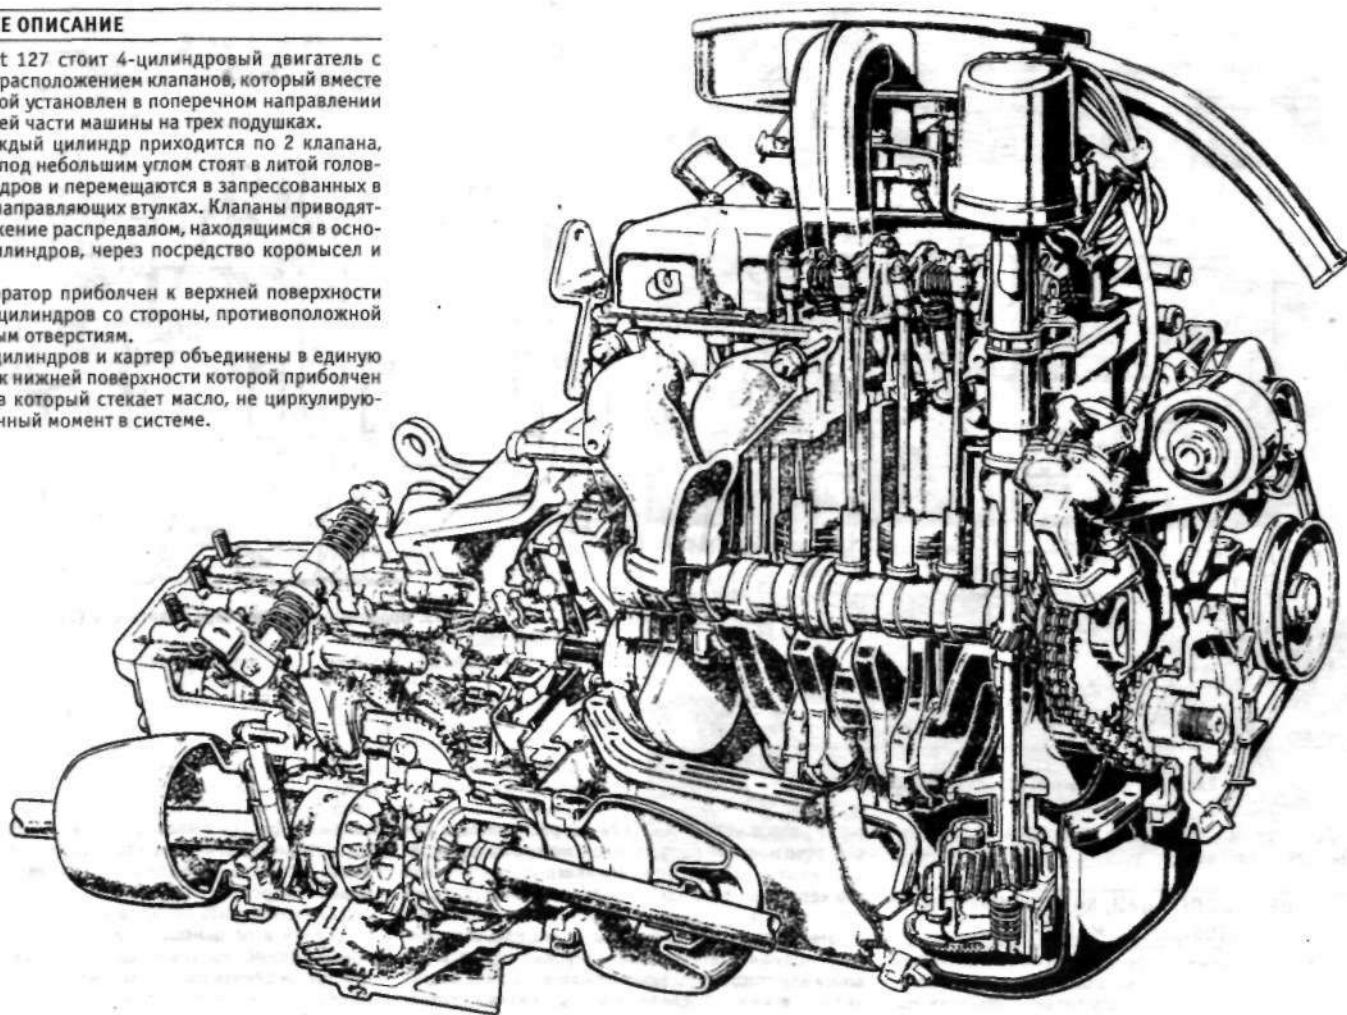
Двигатель 903 см³ и коробка передач (вид в разрезе).
